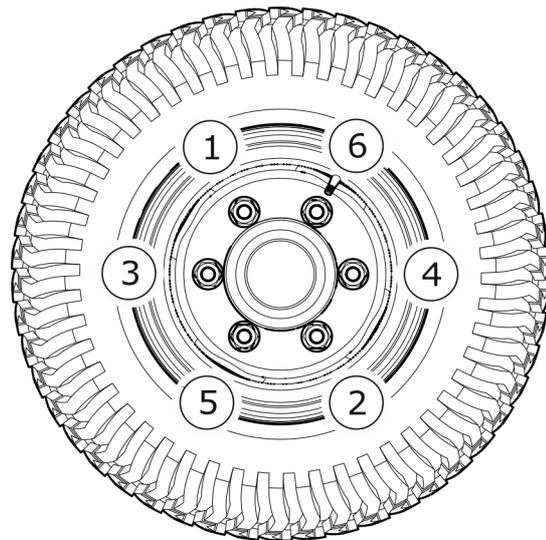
Ordre de desserrage et de serrage des écrous
